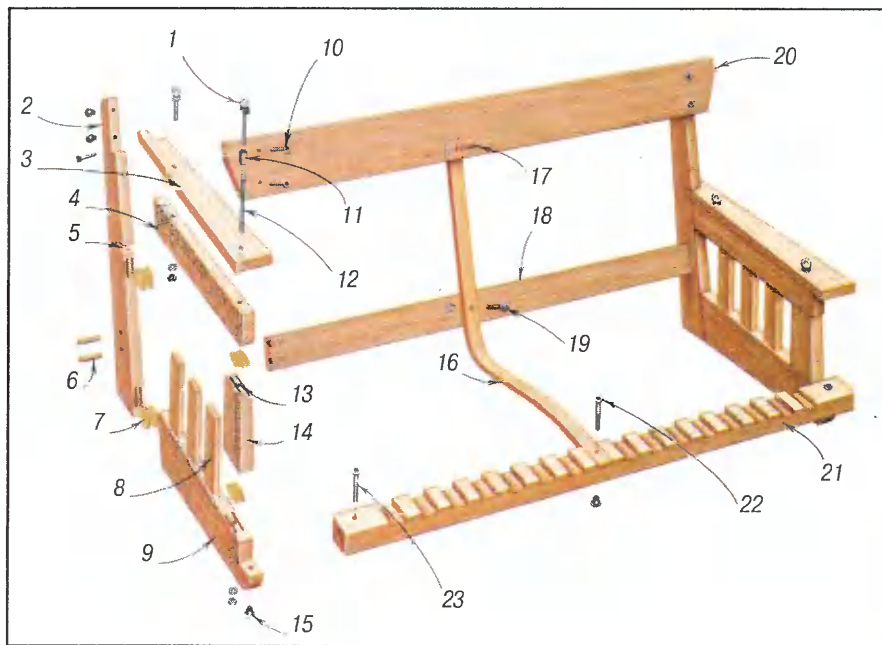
Верандные качели: 1 — болты с проушинами; 2 — задняя опора; 3 — подлокотник; 4 — верхний брусок рамы боковины; 5 — паз для подлокотника; 6 — шканты; 7 — шпонки; 8 — рейки боковины; 9 — нижний брусок боковины; 10 — крепежный болт; 11 — резьбовая втулка; 12 — шпилька; 13 — отверстие под резьбовую втулку; 14 — передний брусок боковины; 15 — декоративный колпачок на гайку; 16 — гнутая рейка сиденья; 17 — шкант; 18 — задняя поперечина сиденья; 19 — шуруп; 20 — верхняя перекладина спинки; 21 — передняя опора сиденья; 22 — шуруп; 23 — винт.
